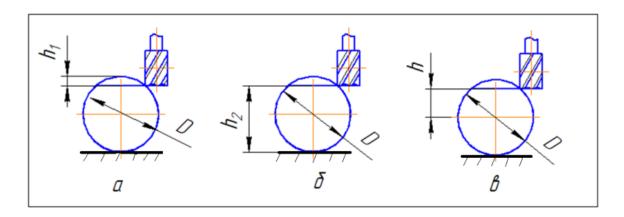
Схемы установки вала на плоскость для фрезерования поперечного паза
